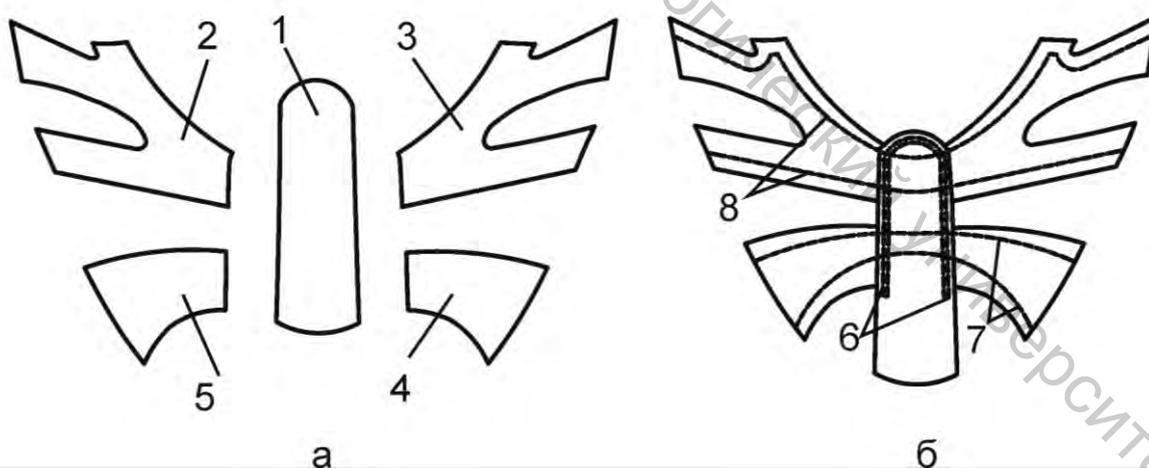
Конструкция заготовки верха сандаальной обуви:
